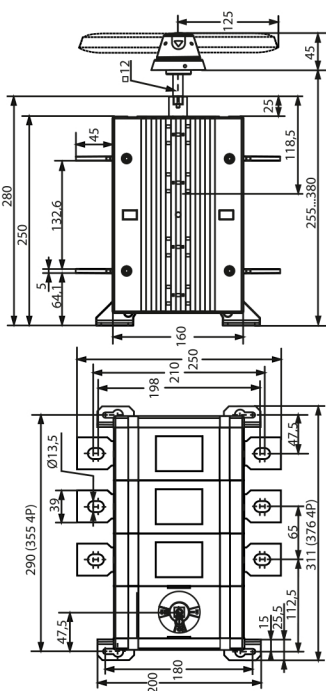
Габаритные и установочные размеры реверсивных рубильников 630-800А
